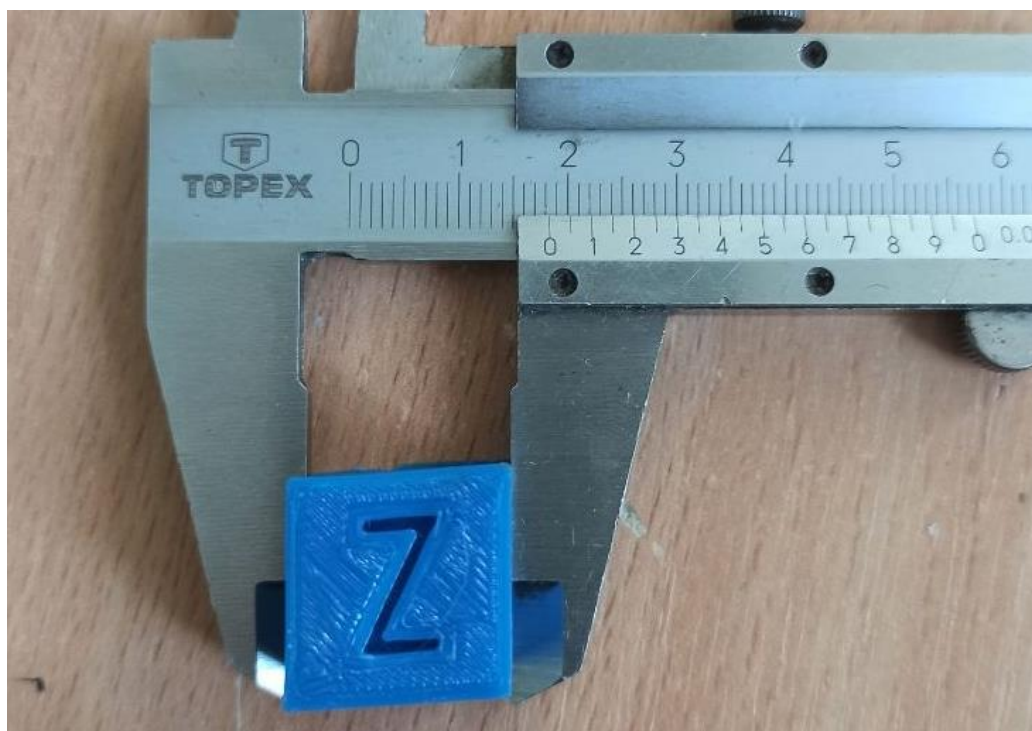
Калібрувальний куб ромбоподібної форми
